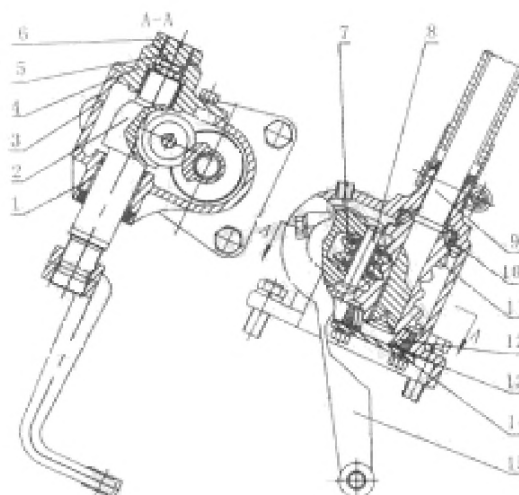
Глобоидный червяк и роликовое рулевое управление.
